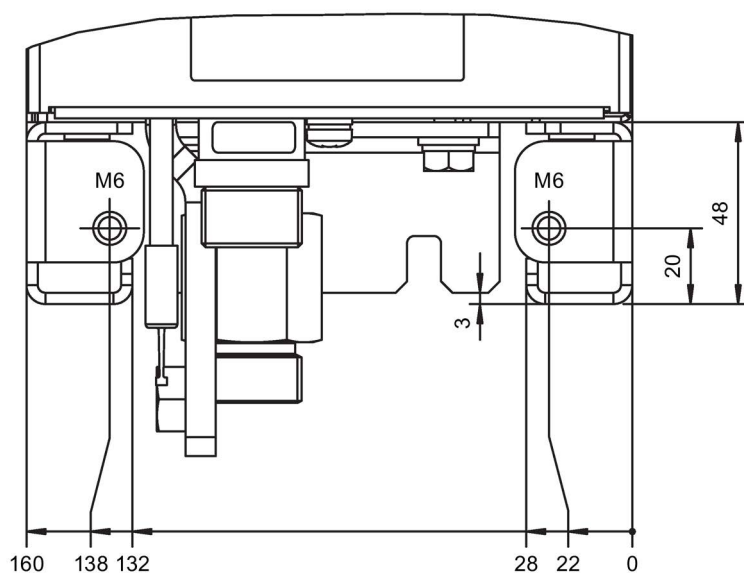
Сечение шины модуля питания Basic, типоразмеры FBL, GBL (размеры указаны в мм)
